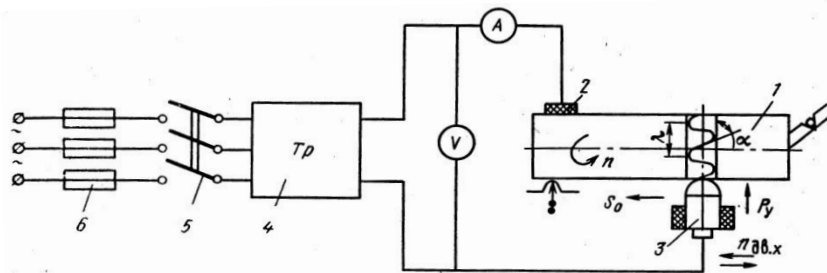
Принципова схема віброелектромеханічного вигладжування поверхонь деталей. 1 – деталь (вал), циліндрична поверхня якої підлягає вигладжуванню; 2 – контактні щітки; 3 – робочий вигладжувальний інструмент; 4 - понижуючий трансформатор.
